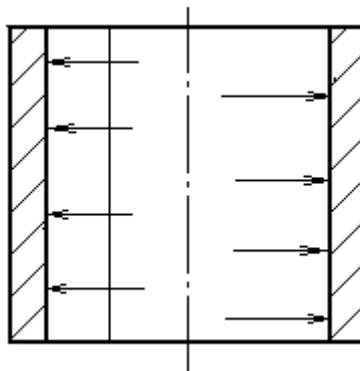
Розрахункова схема обичайки циліндричної
